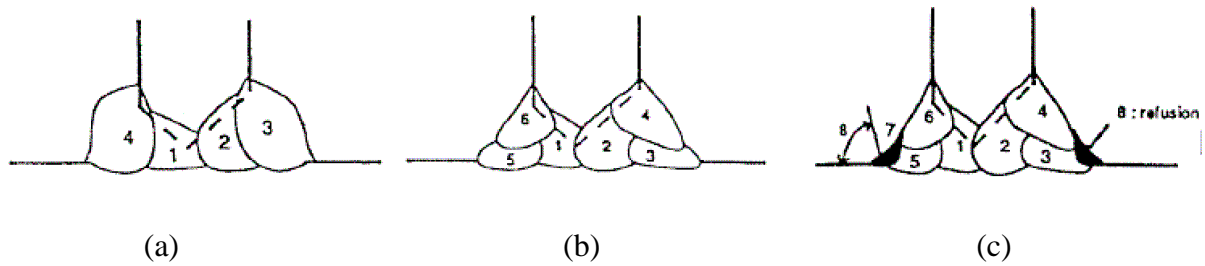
Les différentes procédures de soudure employées pour T-joints acier HSS E690 [TRI 92]. (a).soudage MAG standard (4 passes), (b).procédé amélioré (6 passes et optimisation des paramètres), (c). procédé amélioré plus refusions TIG
